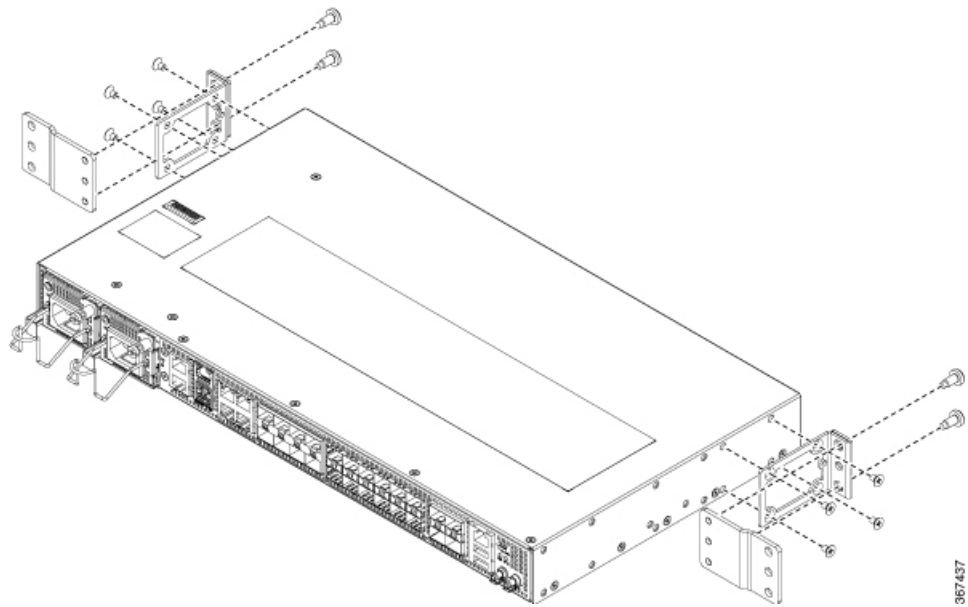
Fixar os suportes de montagem no router para rack ETSI (posição frontal)
